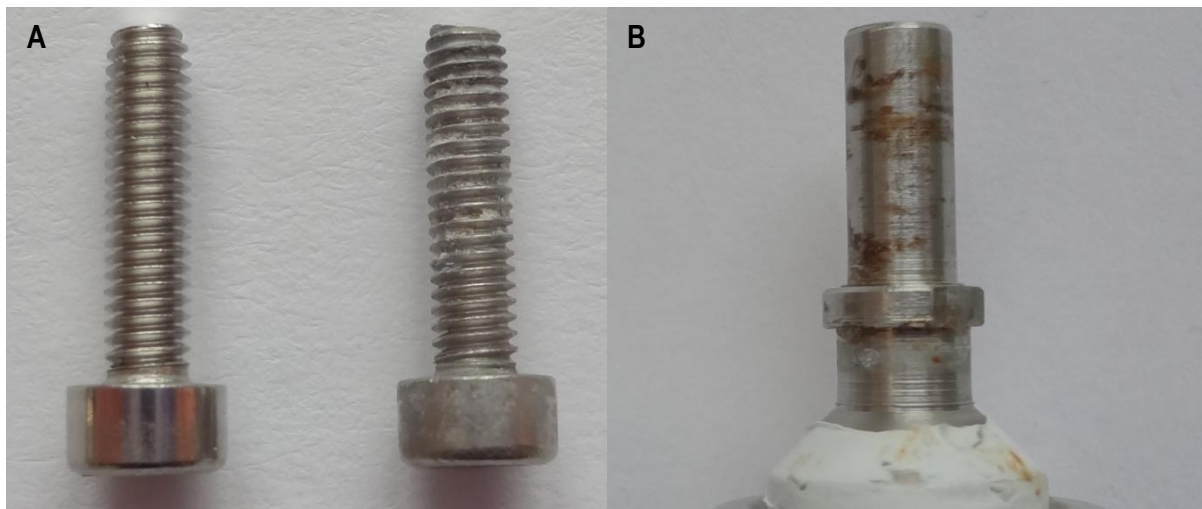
A: Edelstahlsschrauben ohne und mit weißen Ablagerungen, B: Anschlussstück mit Korrosion
